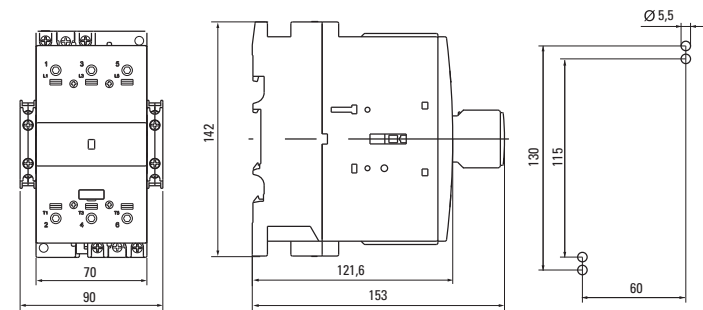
Габаритные и установочные размеры контакторов KM3 80A, KM3 90A, KM3 100A
